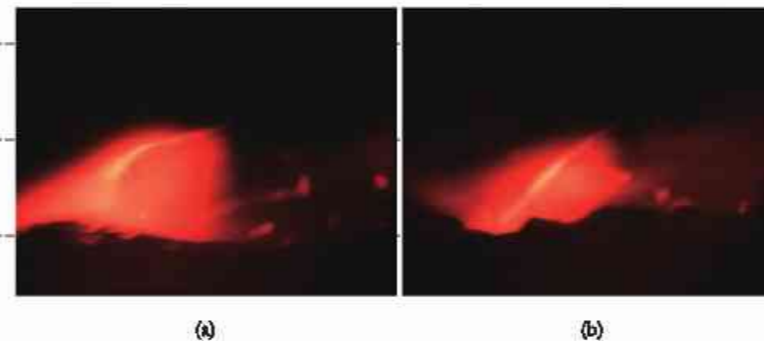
交变磁控高效 GMAW 焊接工艺熔滴过渡行为
